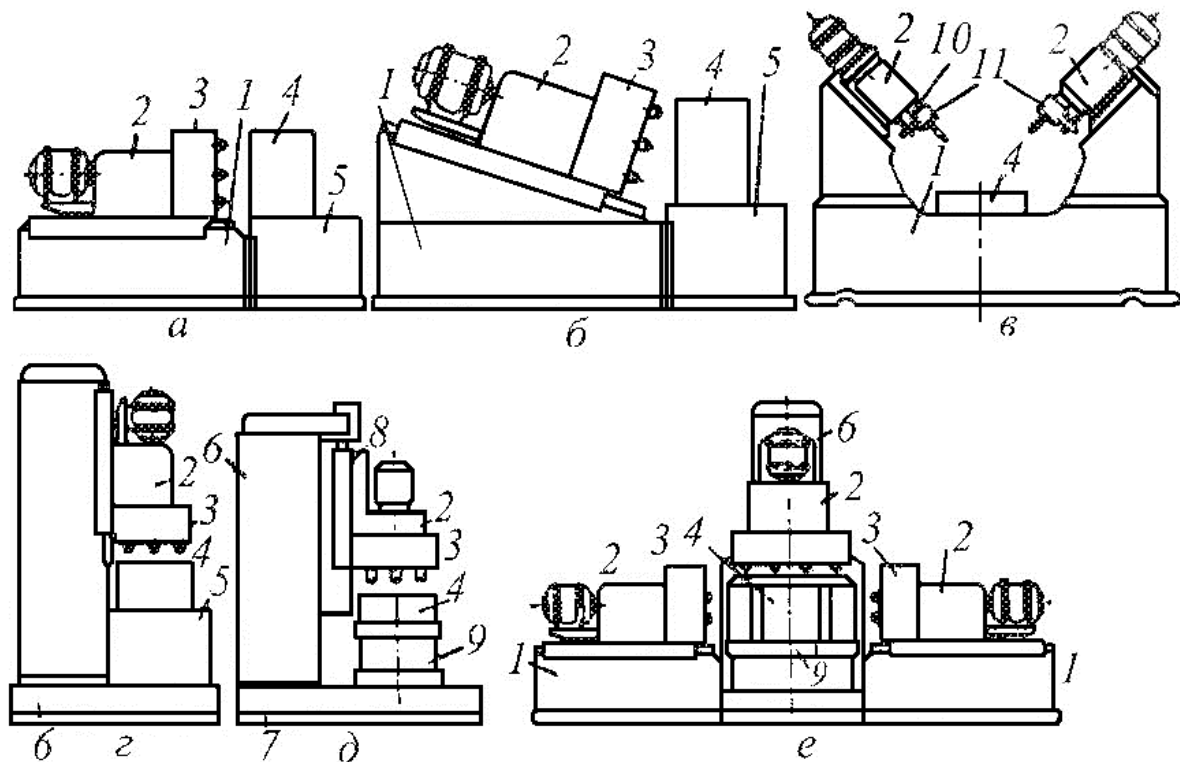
Схеми компоновок агрегатних свердлильних верстатів
